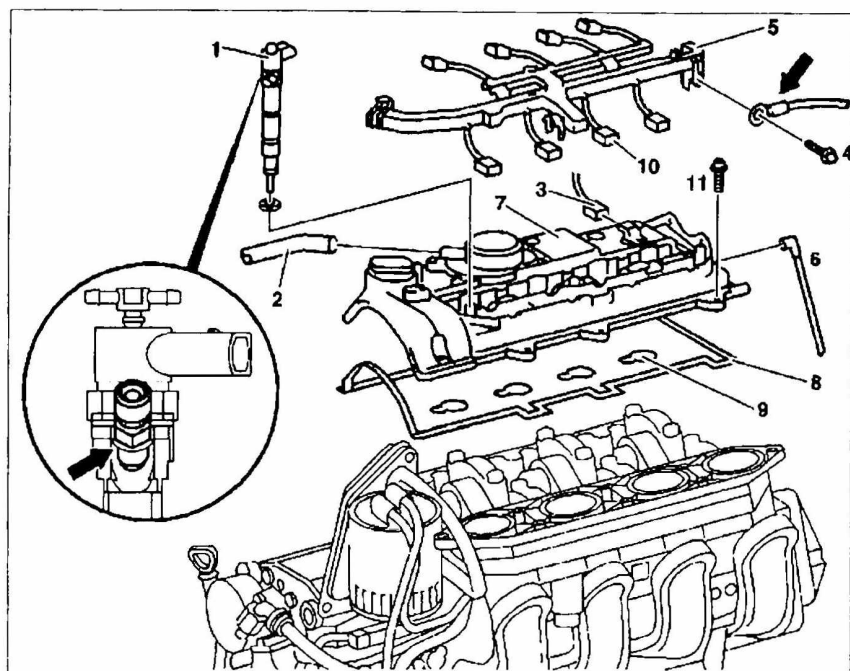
а. Снятие и установка крышки головки блока цилиндров на двигателях 611.981/983/987:
